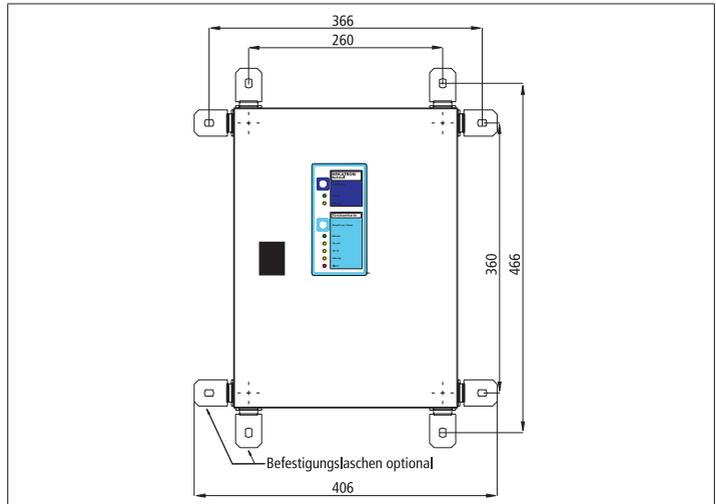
Frontansicht SVG 522 mit Befestigungslaschen
